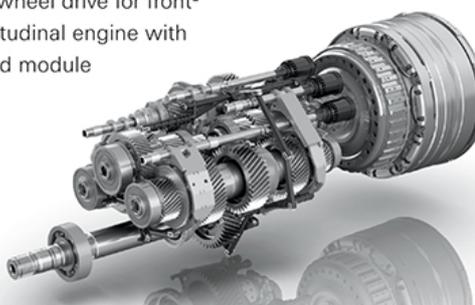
Модульная платформа коробки передач: 8-ступенчатая коробка передач с двойным сцеплением (8DT) предназначена для фронтально-продольного расположения в четырех различных вариантах (стандартный, полноприводный, полноприводный гибрид), каждый в трёх классах крутящего момента до 1000 Нм.
